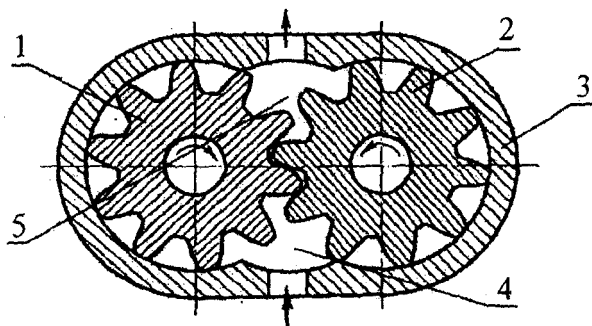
Шестеренный насос с прямозубыми шестернями:
